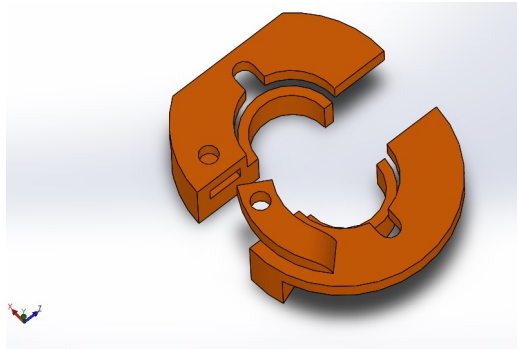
Vista explosionada del utillaje de sujeción del Hotend a la carcasa.
